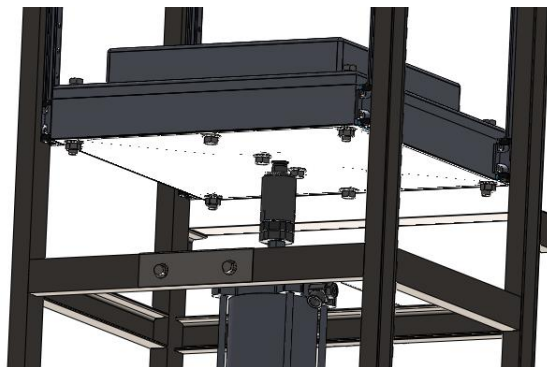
i: Detalle de fijacion placa inferior
